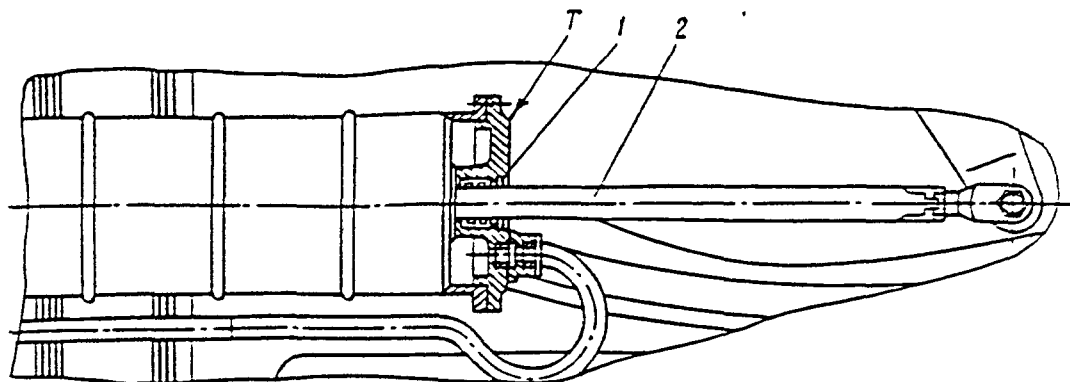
Пневмоцилиндр реверсивного устройства:
